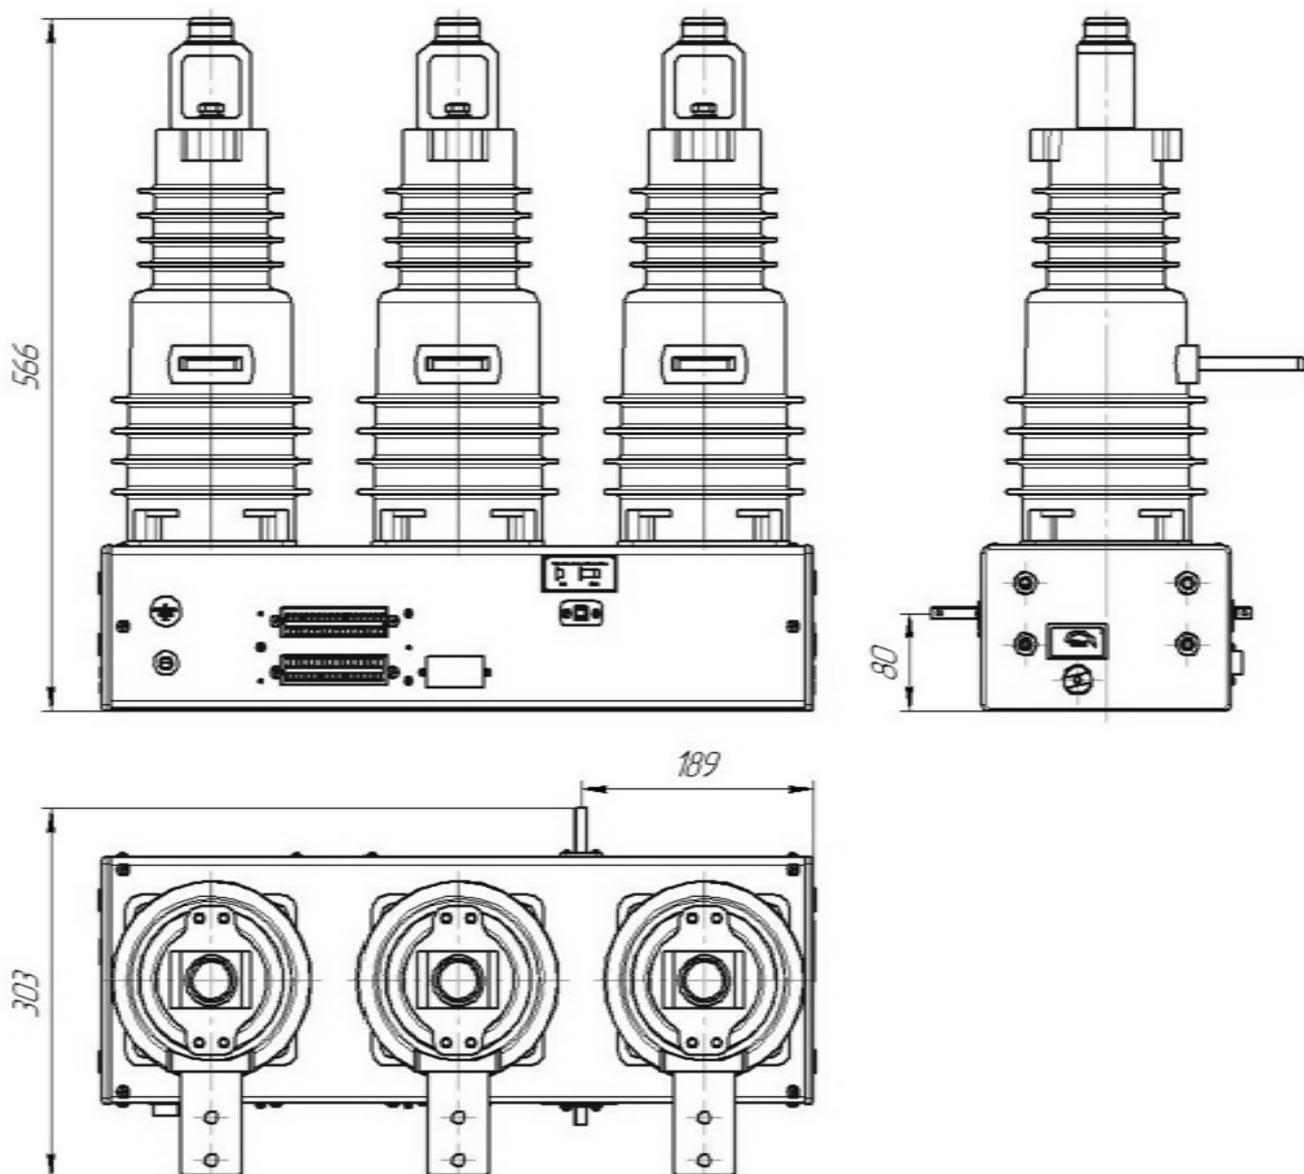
Вакуумный выключатель BB/AST-10-20/XXX-UHL2 -21,22
